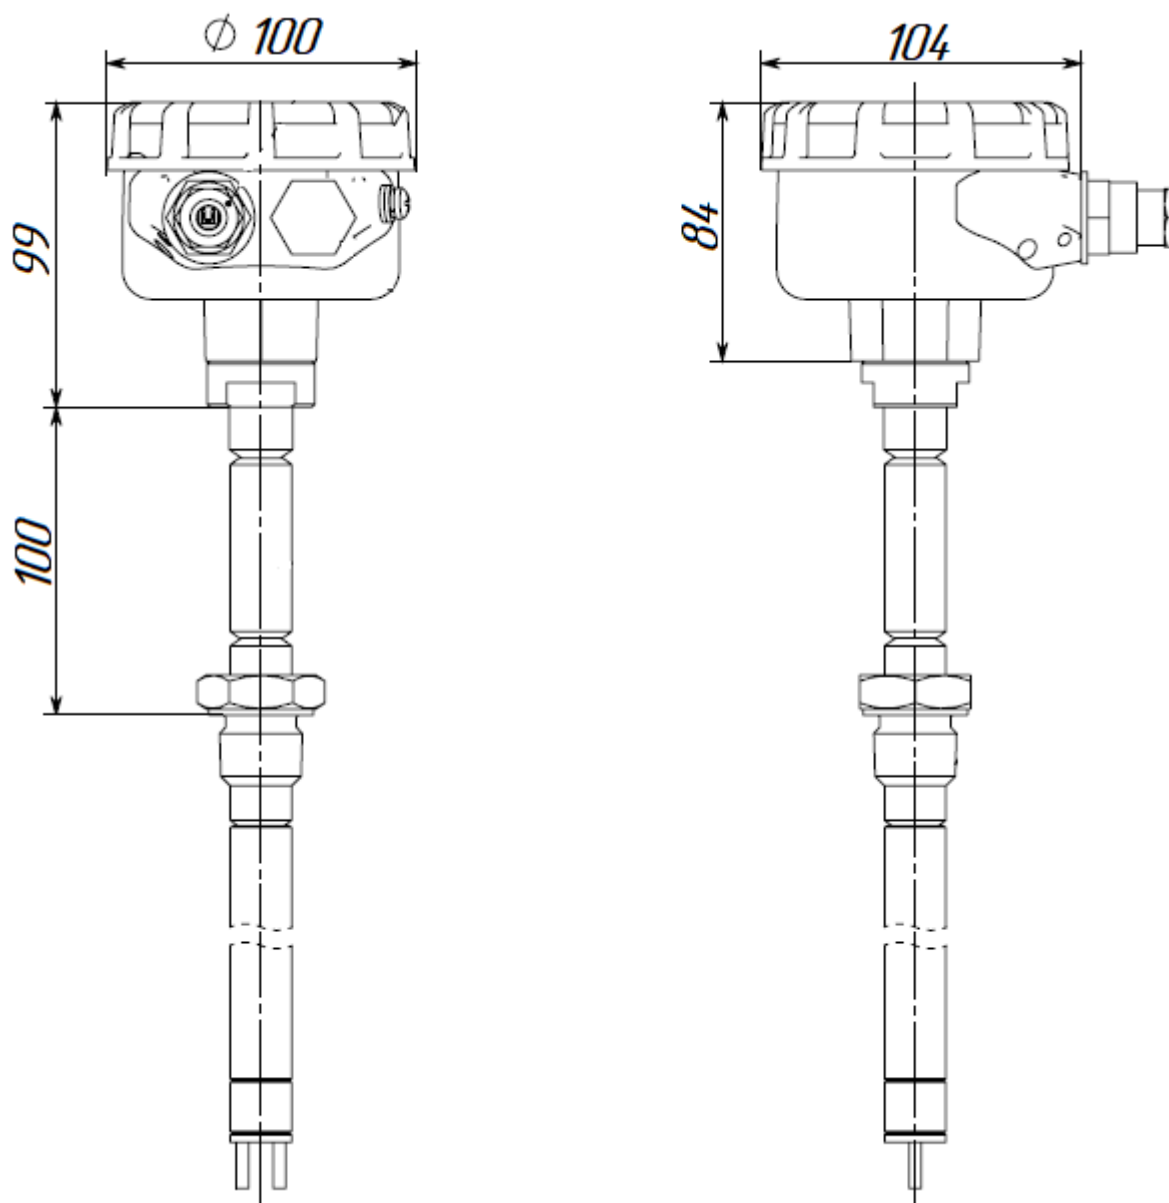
Габаритные размеры корпуса сигнализатора
